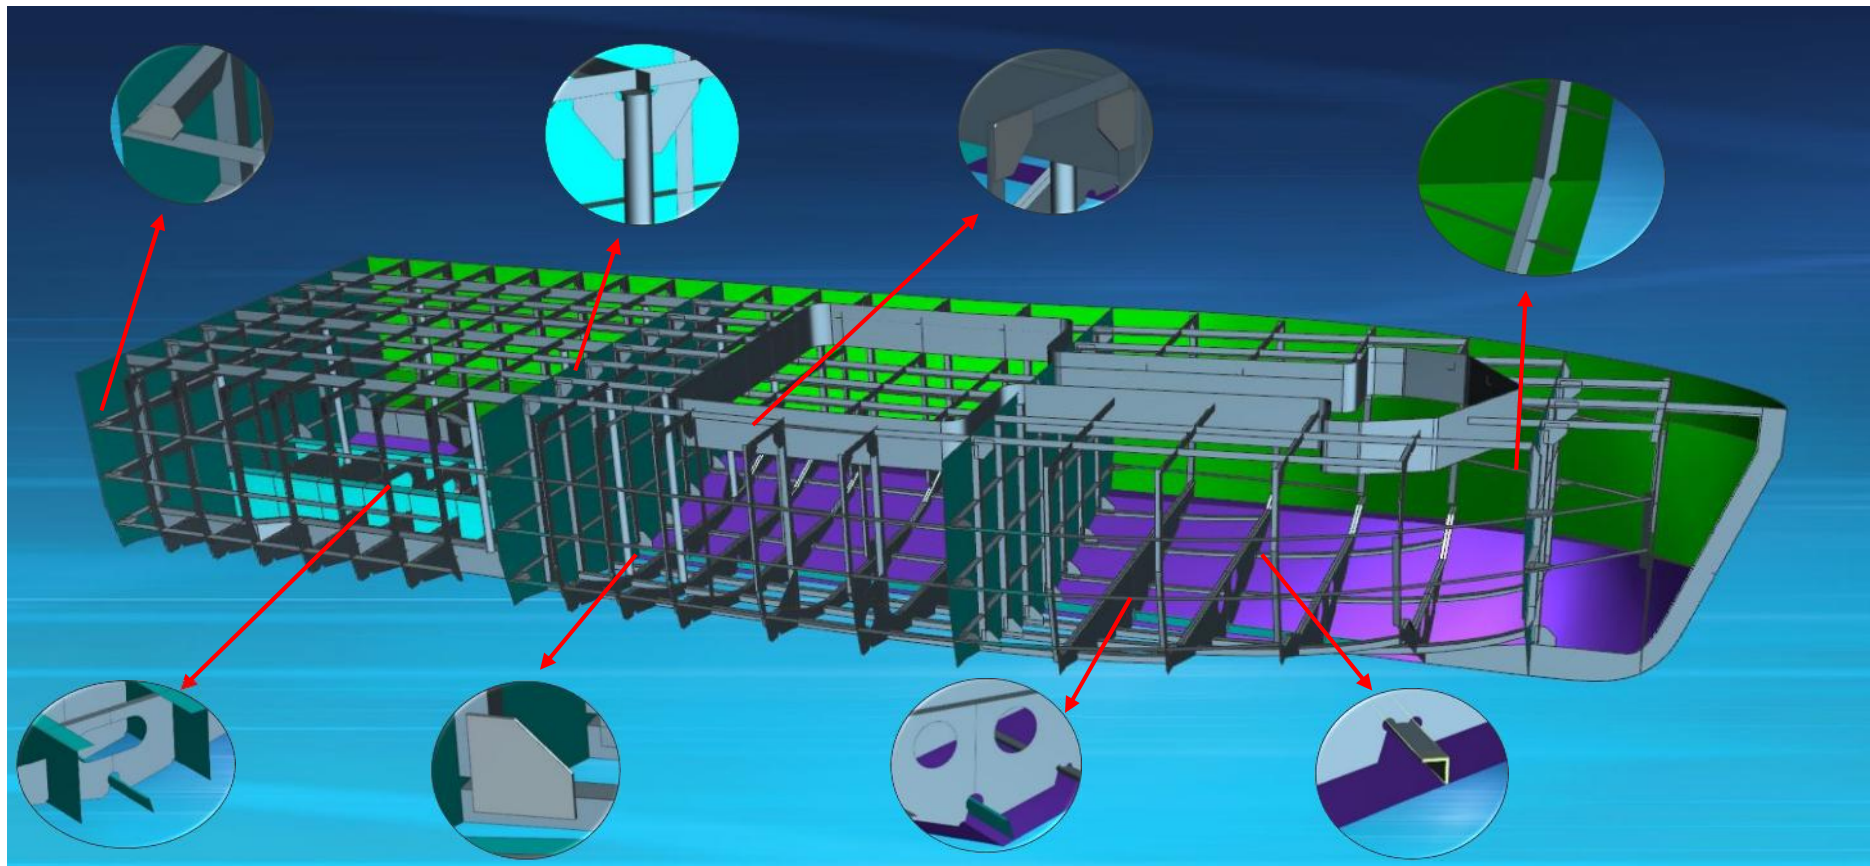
Detalles estructurales del Modelo Geométrico de la Lancha
